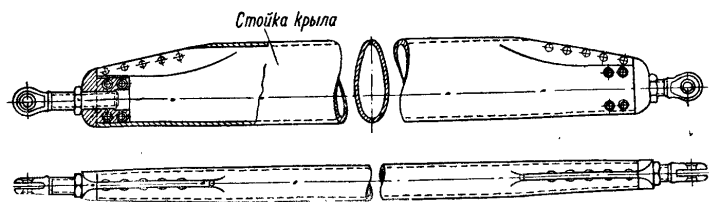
Стойка коробки крыльев (дюралюминовая).
